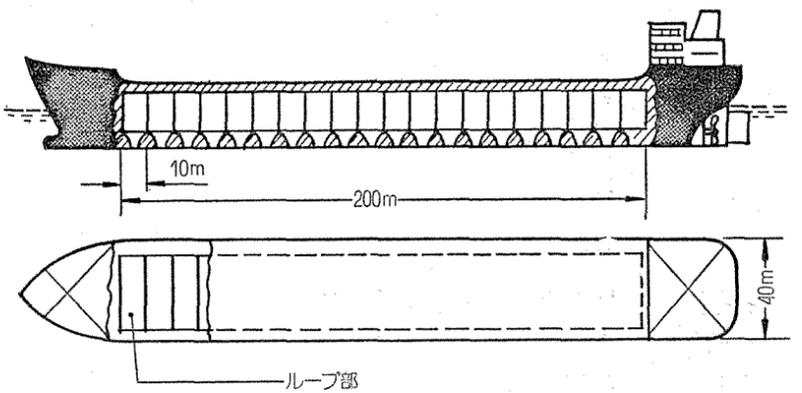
ループ方式海水ウラン吸着船(平面図および縦断面図)
